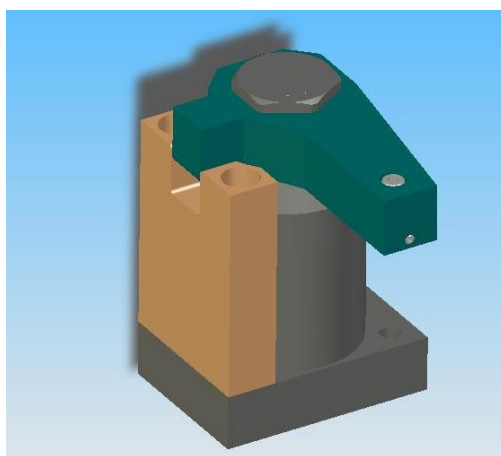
Conjunto Cilindro e Garra de aperto do "Ball-Joint"
